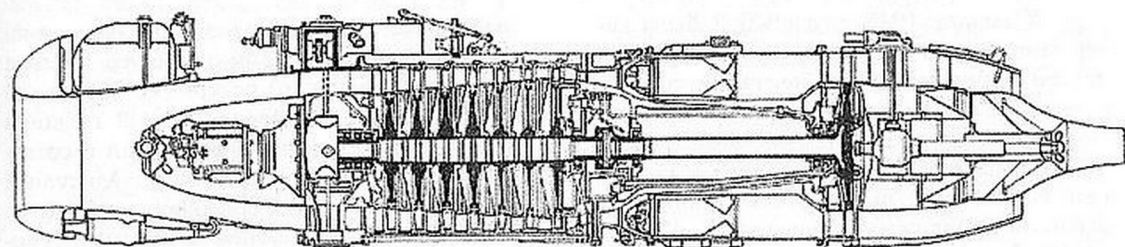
Схема турбореактивного двигателя БМВ-003С
